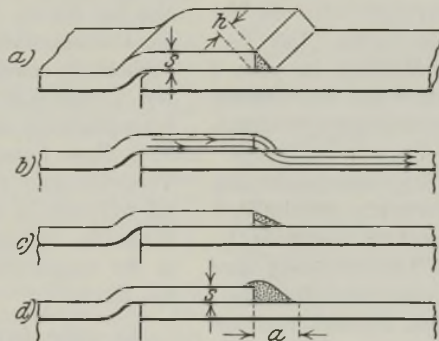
a bis d. Verschiedene Ausführung der Kehlnahtschweißung.
